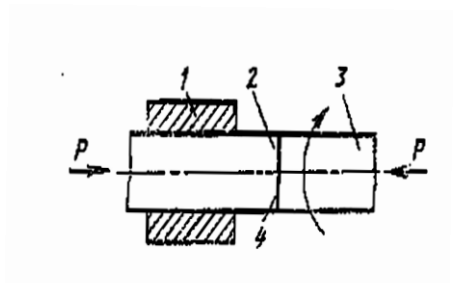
Схема сварки трением: 1 — зажимное устройство; 2 — неподвижная заготовка; 3 — приводимая во вращение заготовка; 4 — поверхность трения.
